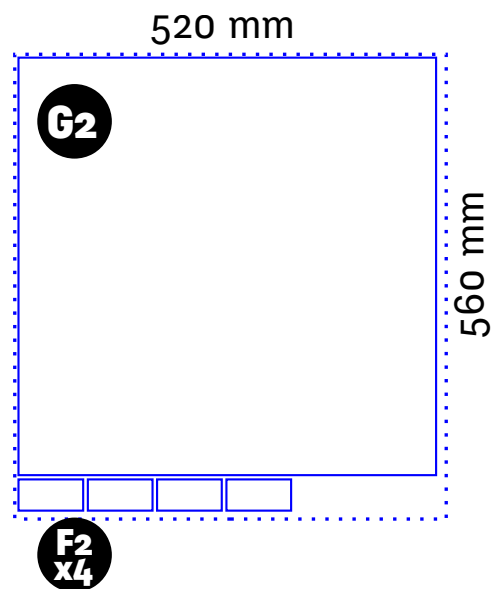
Plan de calepinage conseillé pour les pièces G2 et F2, dans un panneau de contreplaqué épaisseur 10 mm de dimensions 0.56 x 0.52 m.
